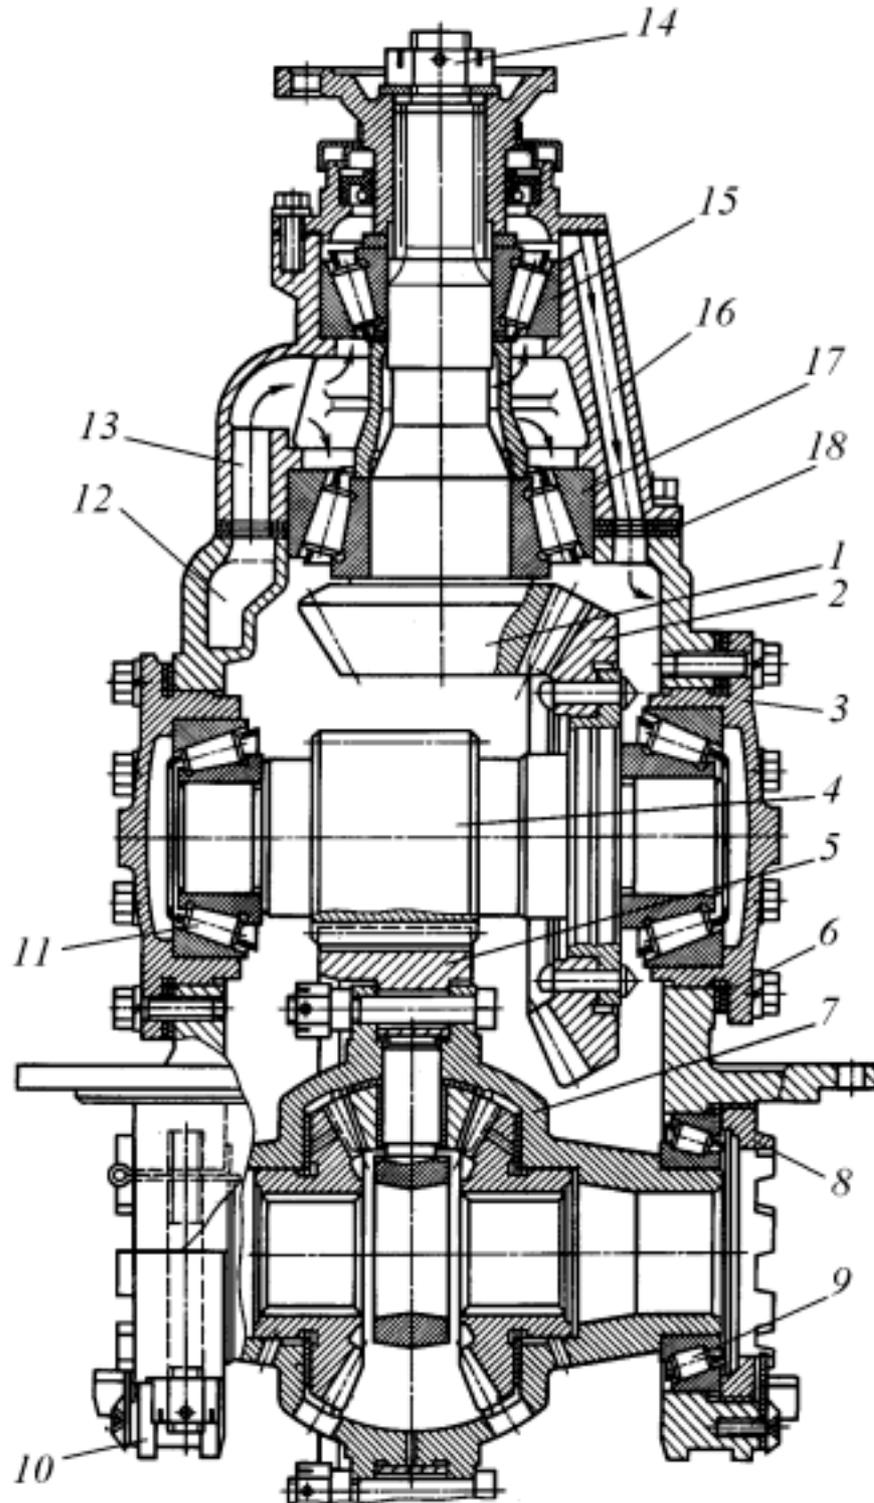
Двойная центральная передача с валами, расположенными в одной плоскости
